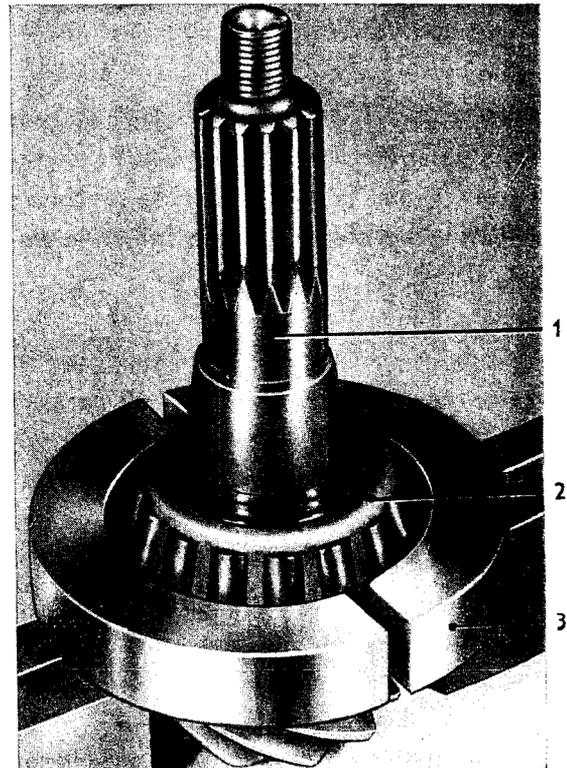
Inneren Laufring mit Kegelkäfig vom Antriebkegelrad abdrücken
